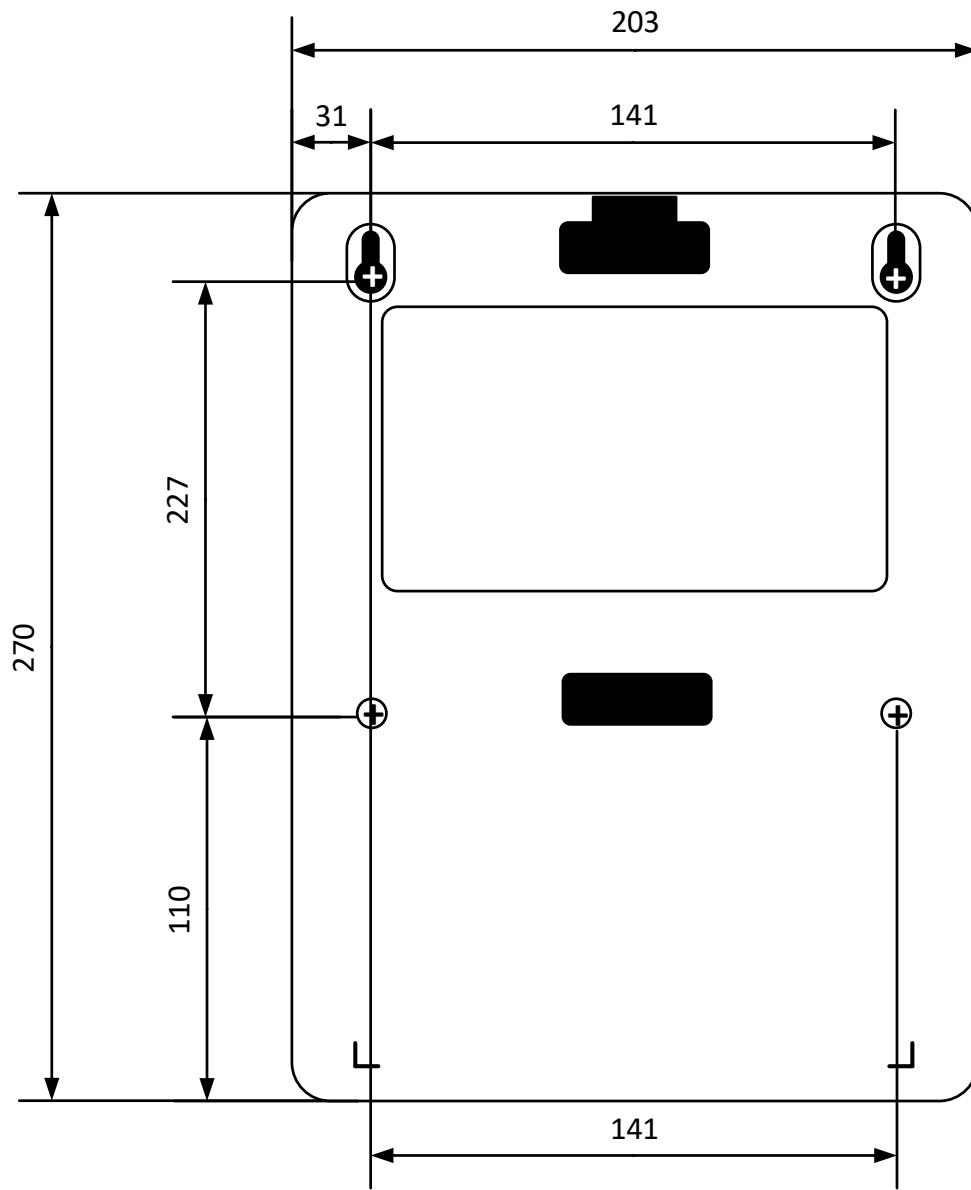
Разметка отверстий для крепления приборов КОП-01 исп.3, КОП-04 исп.2-3
